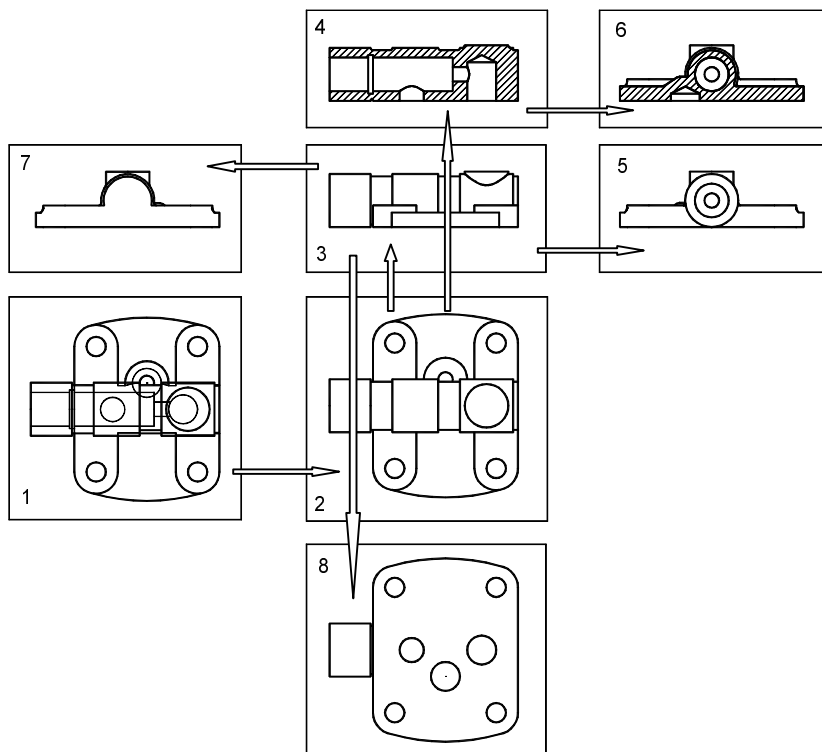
Формирование видовых окон для построения чертежа крышки
